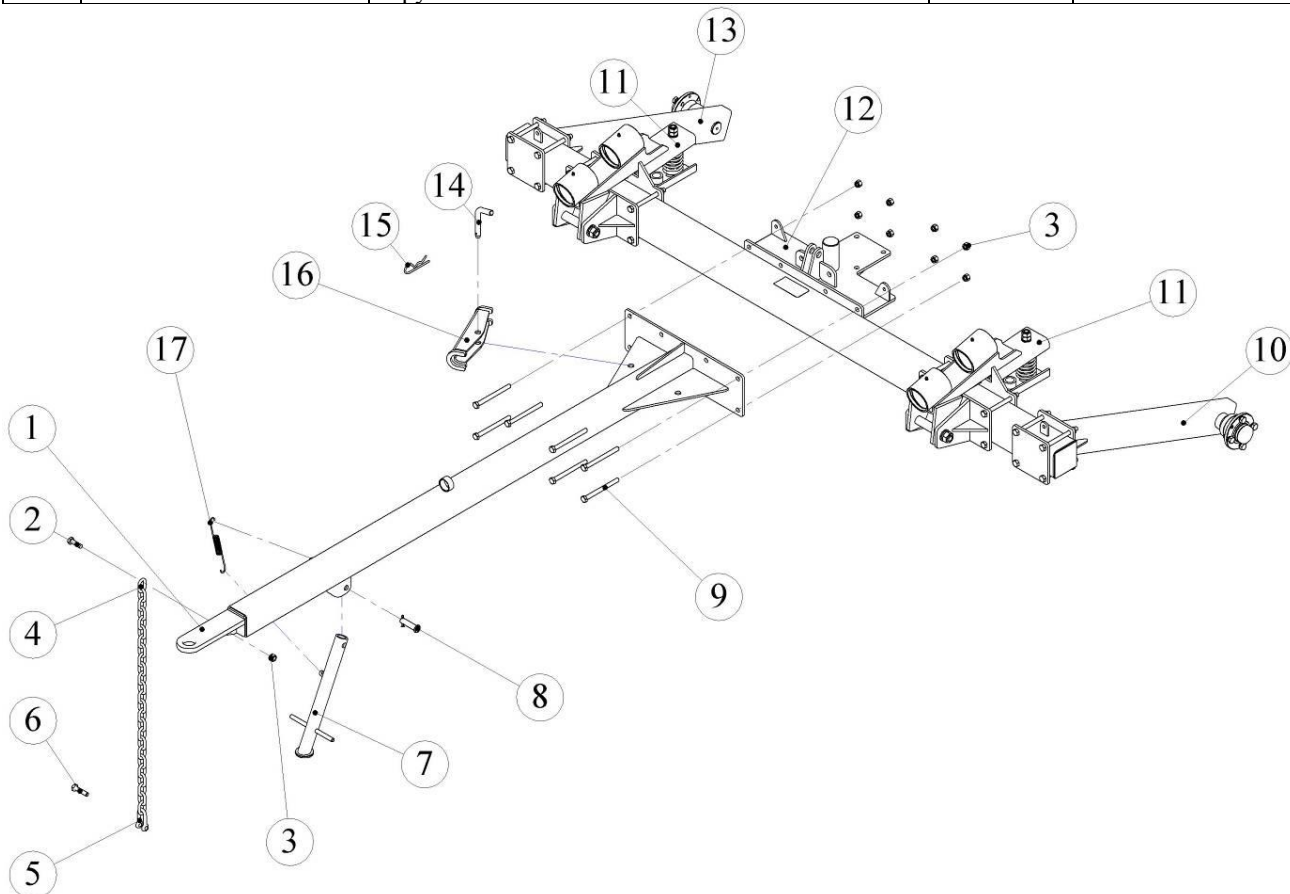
Основная балка с дышлом, кронштейном гидроцилиндра, балками опорных колес и кронштейнами секций
